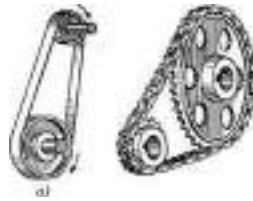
Передачи с гибкой связью: а — ременная; б — цепная
